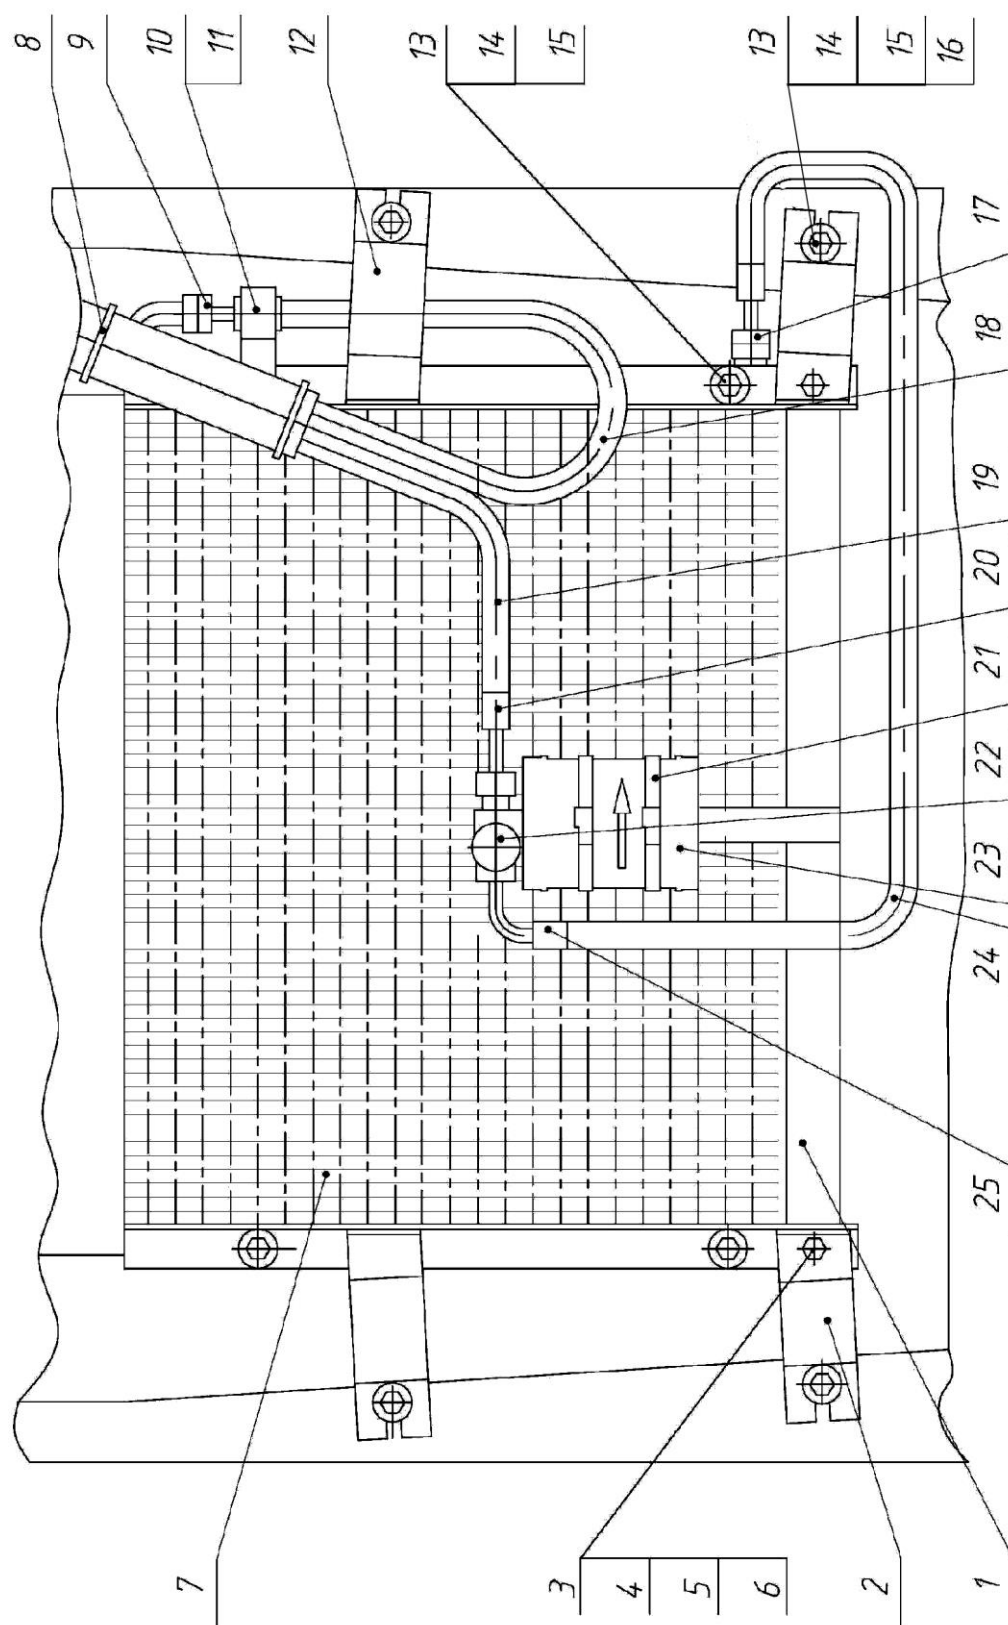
Установка конденсатора и фильтра-осушителя
